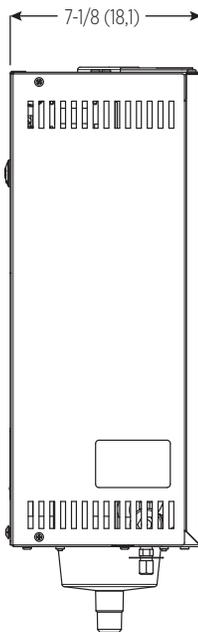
DIMENSIONS DE L'HUMIDIFICATEUR (POUCES [CM])
